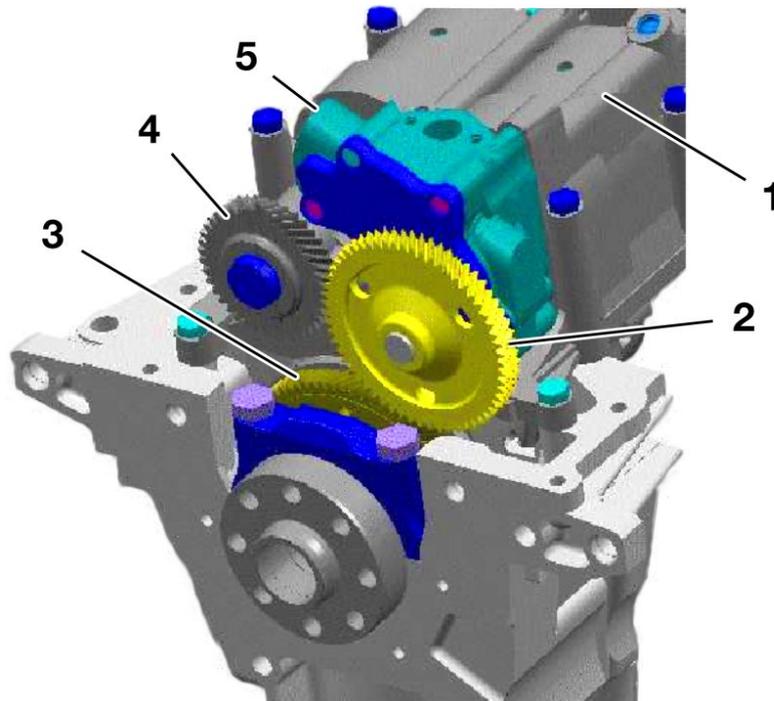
Ausgleichswellengehäuse (Draufsicht)
